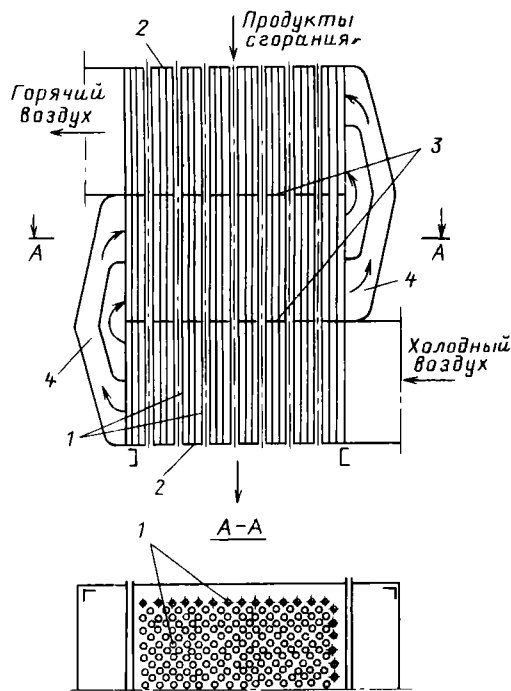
Рекуперативный трубчатый трехходовой воздухоподогреватель: 1 — трубки; 2 — трубные доски; 3 — перегородка; 4 — перепускные короба
